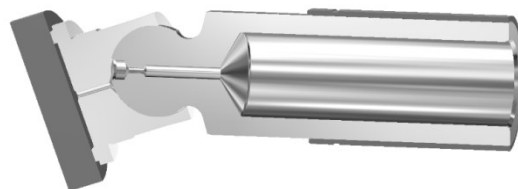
Подготовленная для расчета сборка плунжера (разрез)
